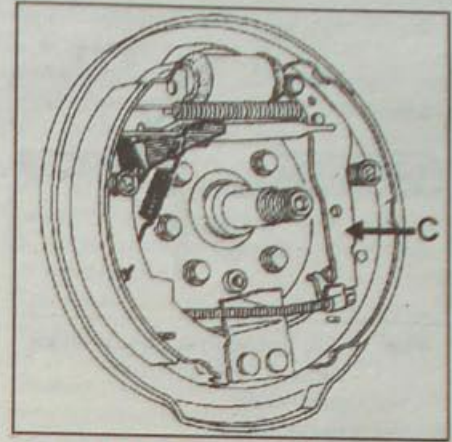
Правильное расположение рычага (С) привода стояночного тормоза на тормозной колодке
